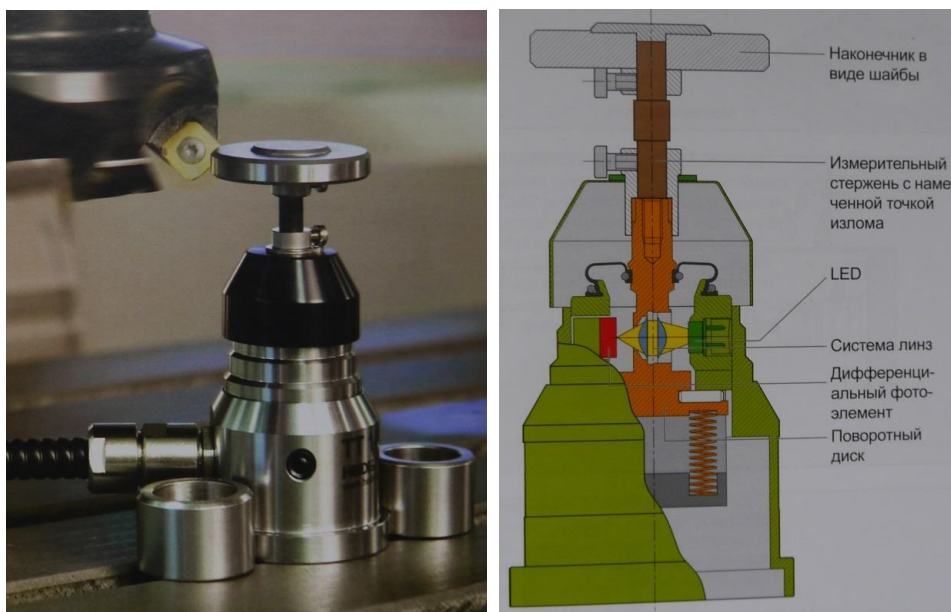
Загальний вигляд та принципова схема щупа ТТ140 та безконтактного оптичного сенсора
